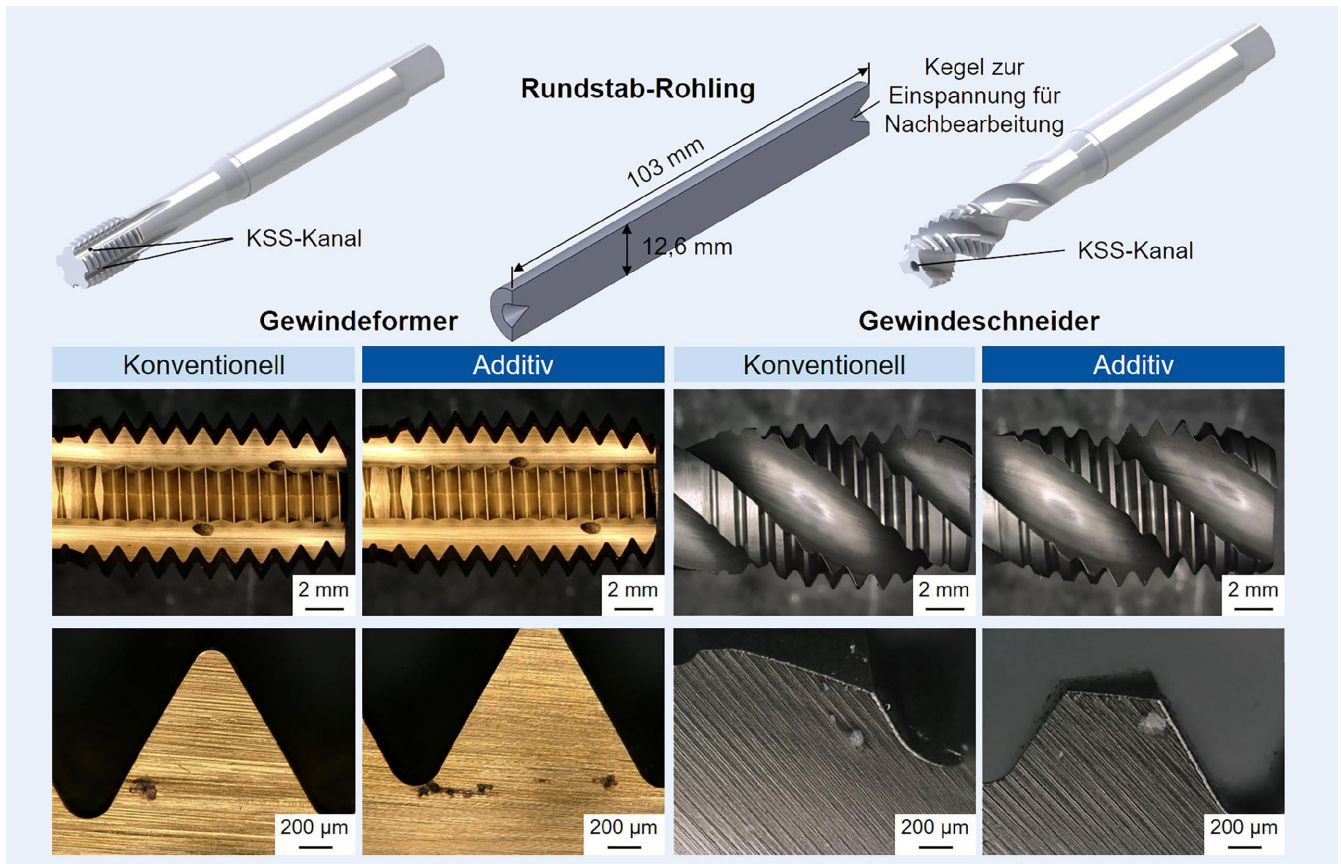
Werkzeuggeometrien Gewindeformer und Gewindeschneider und beispielhaft dargestellte qualitative lichtmikroskopische Bewertung.
